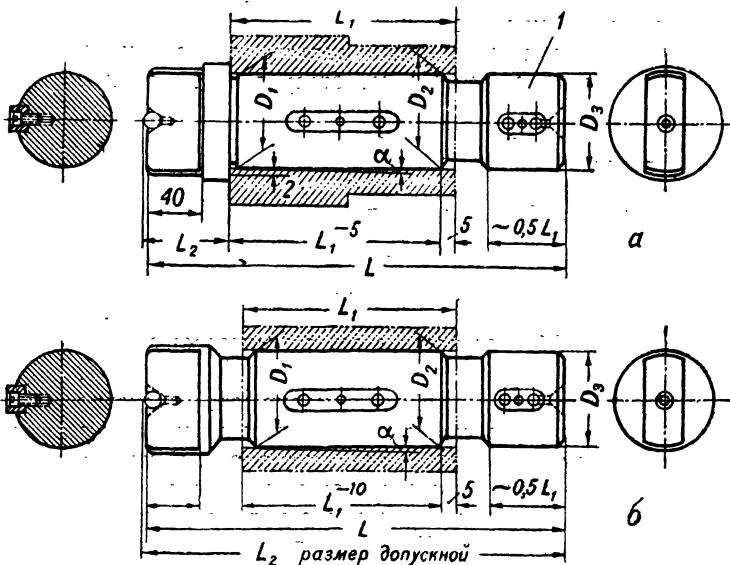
Оправки для изделий, устанавливаемых под прессом.
